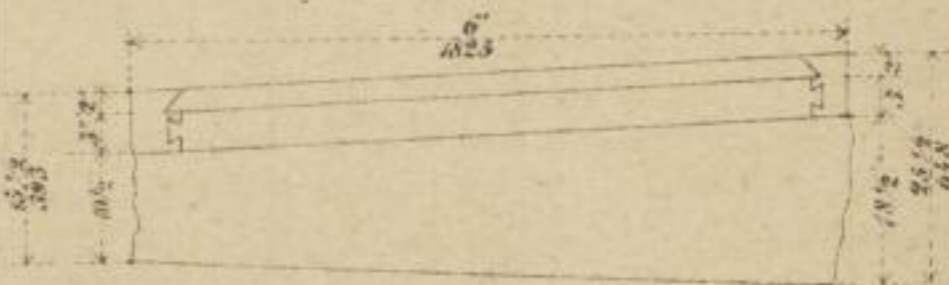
Grundplatte mit Rahmen und Deckplatte für Compoundplatte obiger Dimension.
